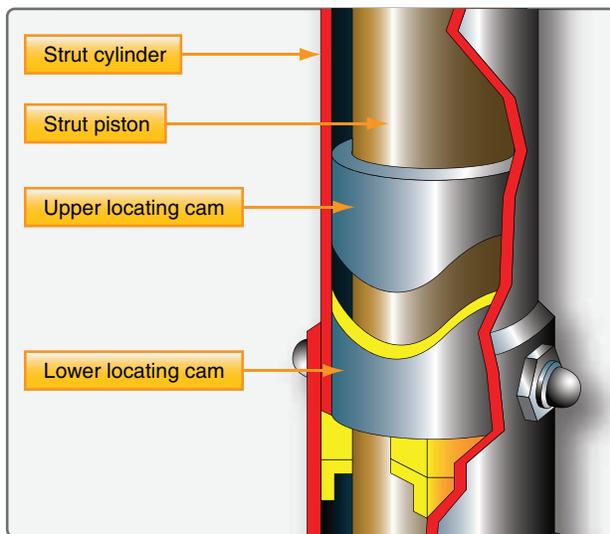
Vista de corte da centering cam interna de um trem de pouso do nariz.
